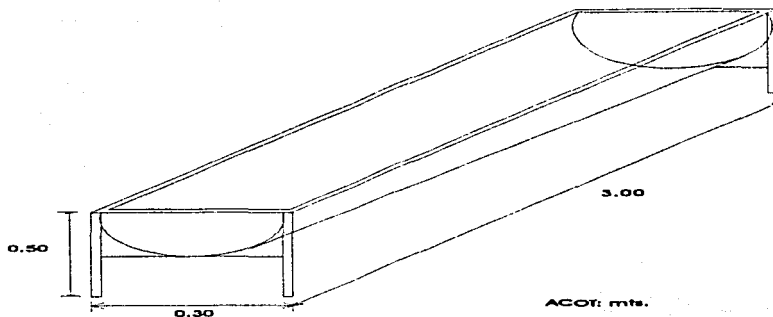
Comedero móvil construido con tubos cortados por la parte media longitudinal y soporte de ángulo.
